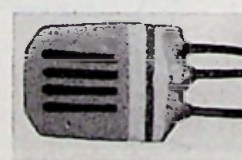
De uitstekende draadeinden worden ook aan de achterzijde langs het plexiglas gebogen. Hierbij dient ervoor te worden gezorgd dat de koperen stripjes elkaar niet raken.
